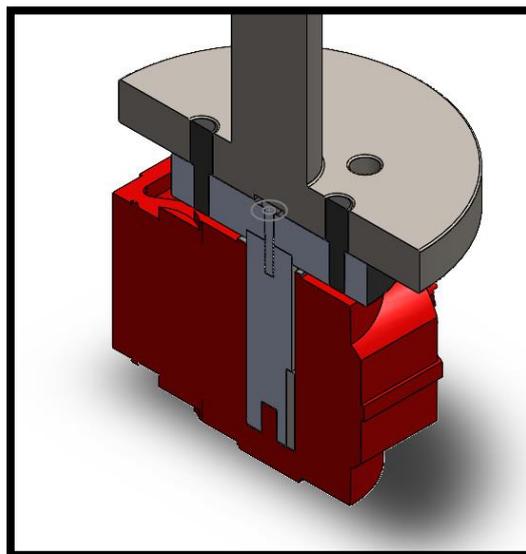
Corte por sección del conjunto. Fuente: Captura SolidWorks
